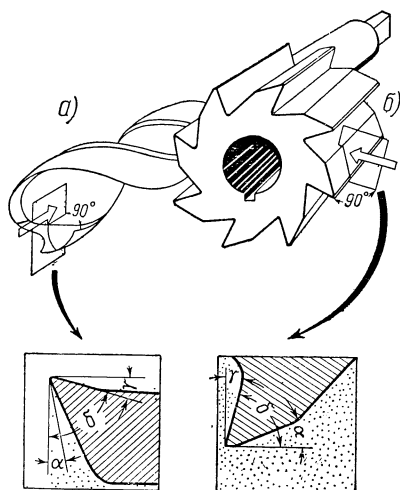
Углы режущей части спирального сверла (а) и цилиндрической фрезы (б).
